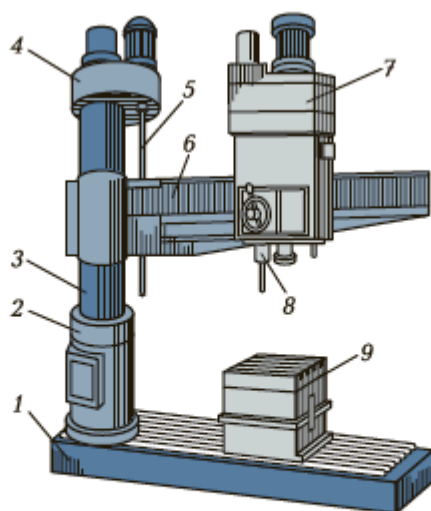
Радиально-сверлильный станок общего назначения:
